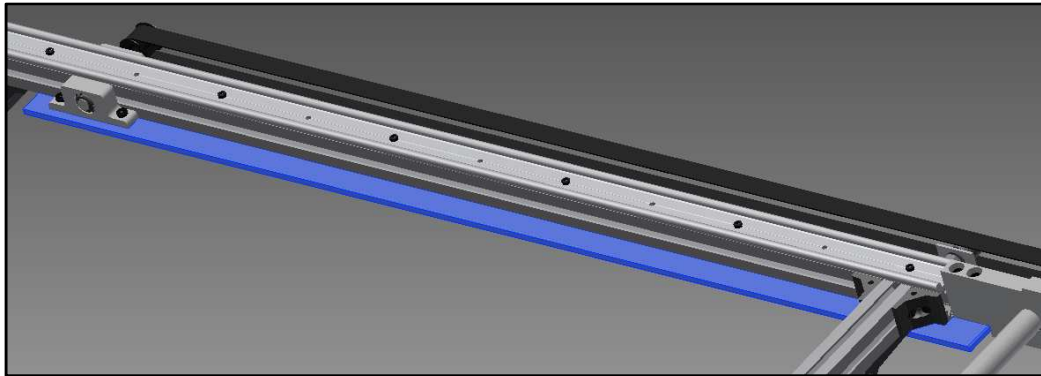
Chapa de apoyo estructural derecho en el montaje.
